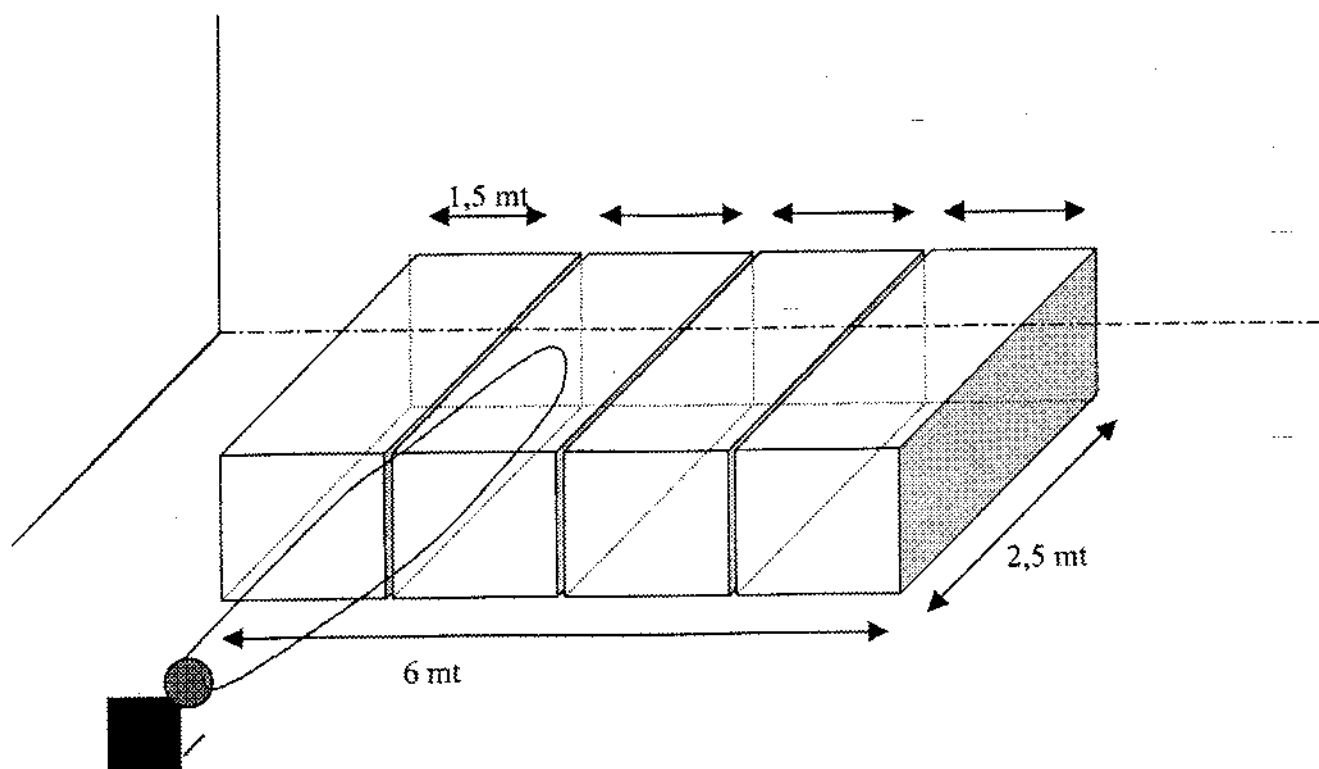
Разделка блоков-заготовок на блоки товарных размеров.
